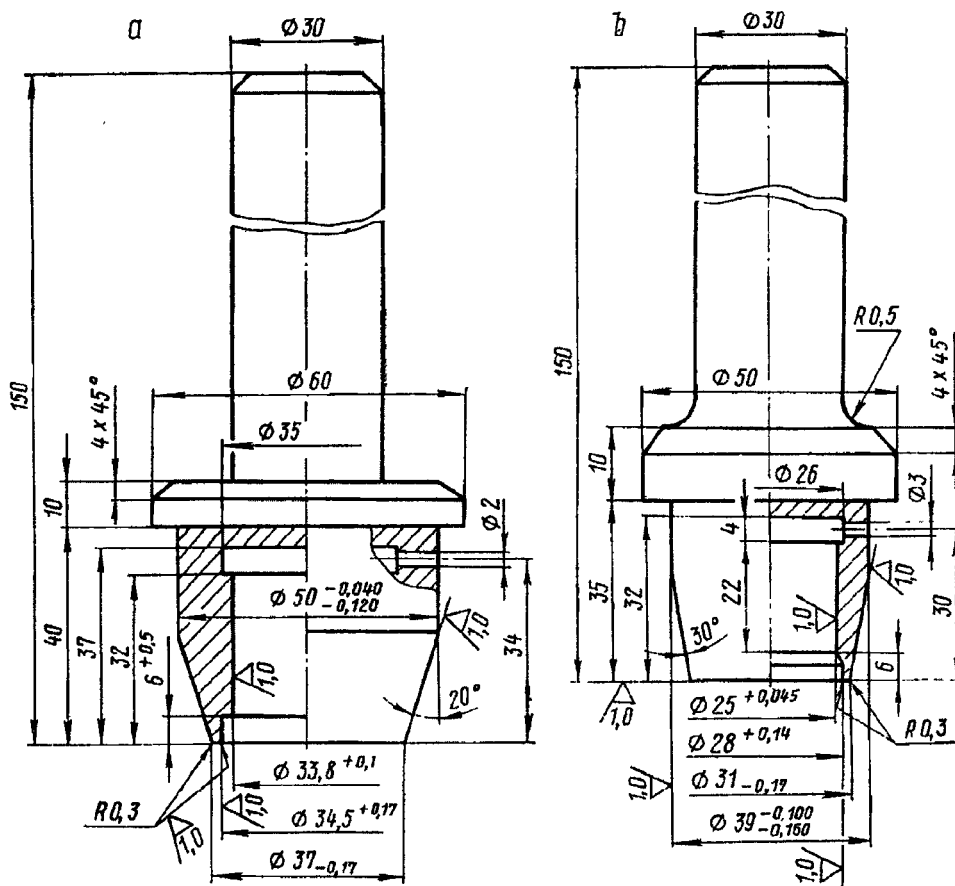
Оправки для напрессовки торцовых уплотнений на крестовины карданных валов приводов:
